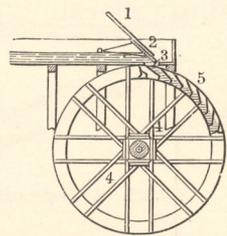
Oberschlächtiges Wasserrad mit Spansschütze.
